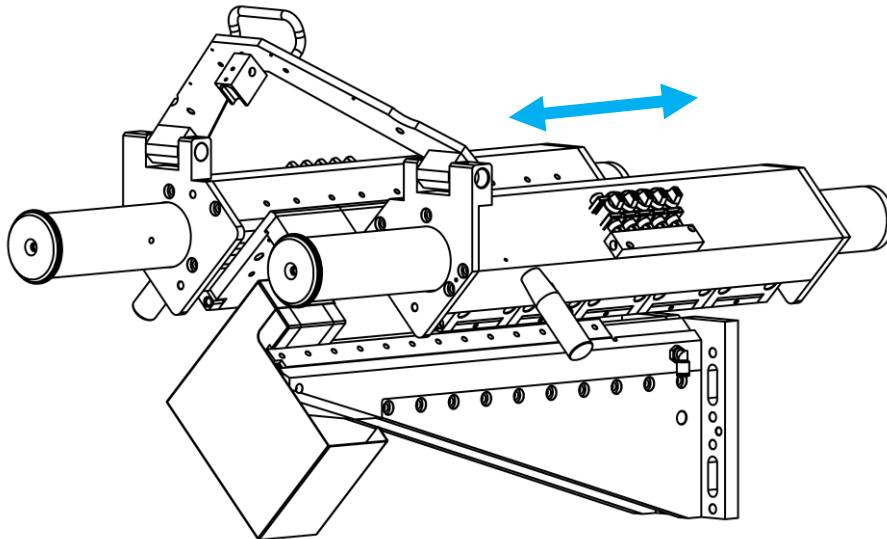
Verschiebbares Außenspannsystem zum Einlegen abgekanteter Bauteile bis 100 mm Schweißlänge (Standard Innenspannwerkzeugsatz) ohne Holmhub.
